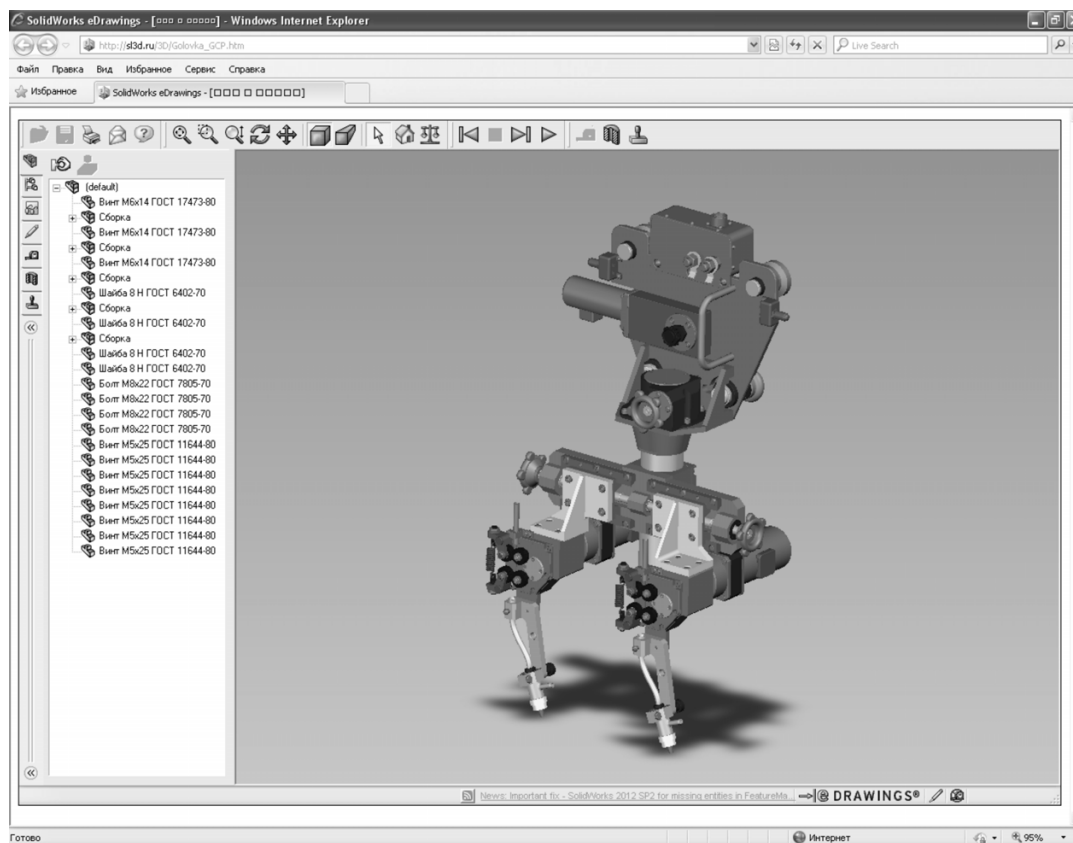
3D-модель к термину «Сварочная полуавтоматическая головка ГСП-4»
